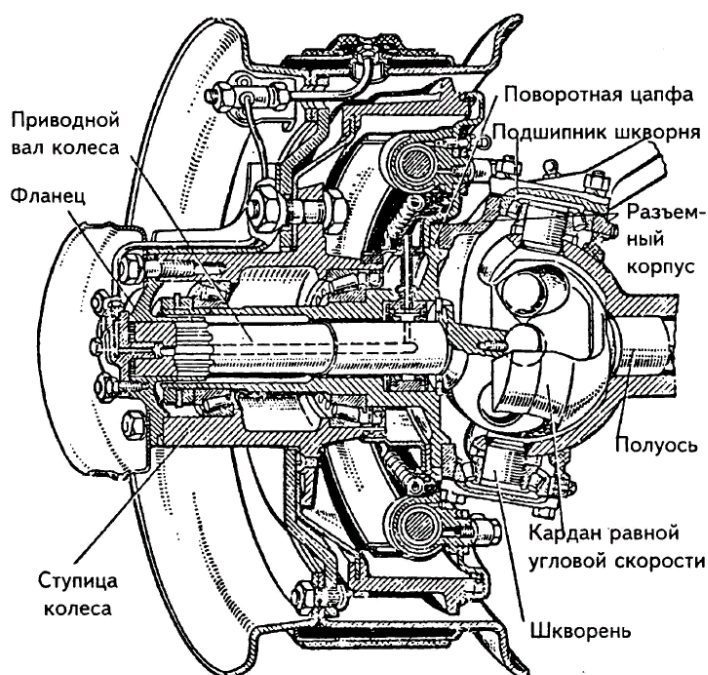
Привод управляемого ведущего колеса автомобиля ГАЗ-66
